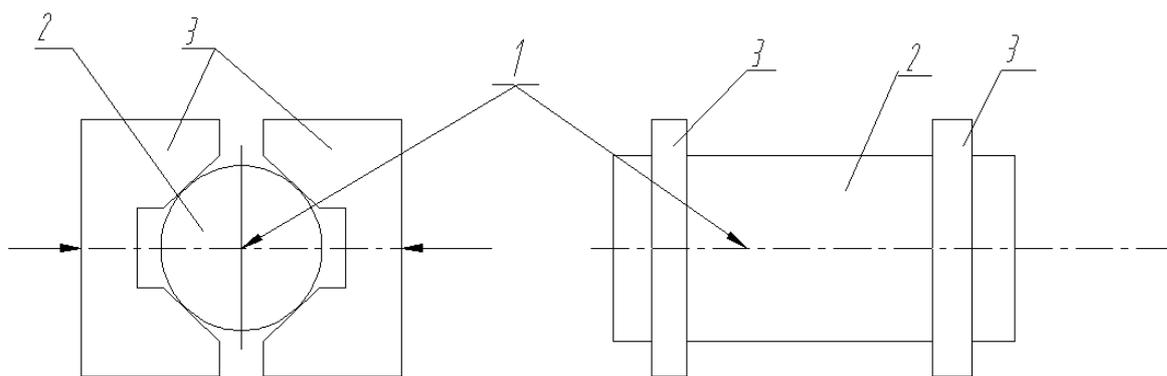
База – ось. 1 – база; 2 – деталь; 3 - губки самоцентрирующих тисков
